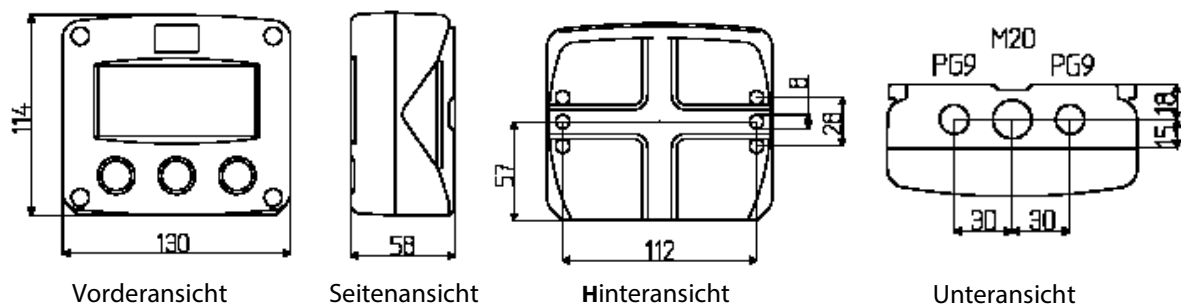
Abmessungen für Option HA: IP67 Aluminium Feldgehäuse mit 2xPG9 und 1xM20 Bohrung
